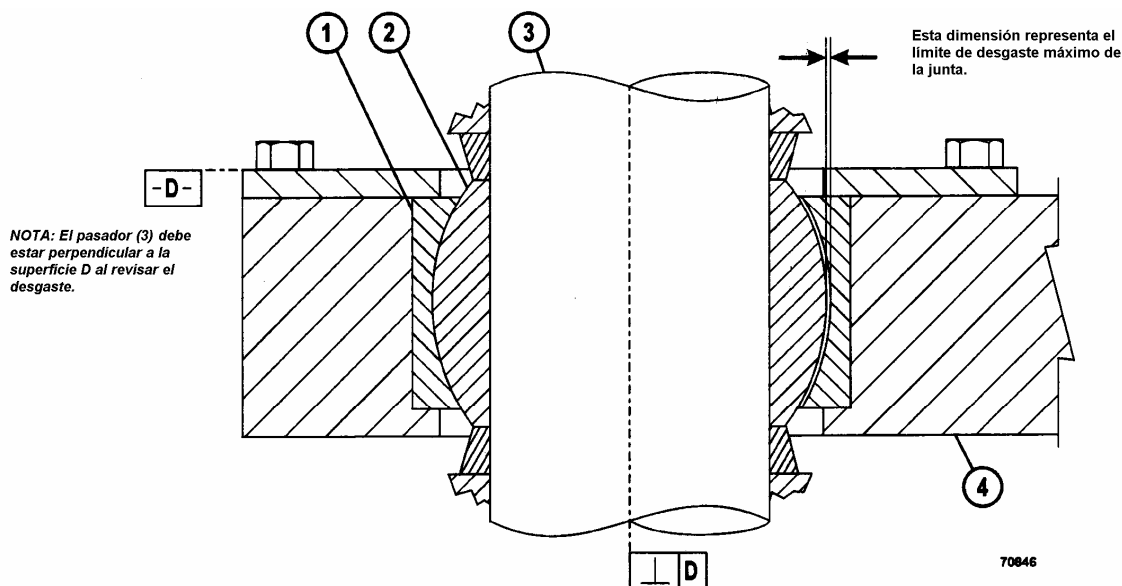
LIMITES DE DESGASTE DEL RODAMIENTO ESFERICO
